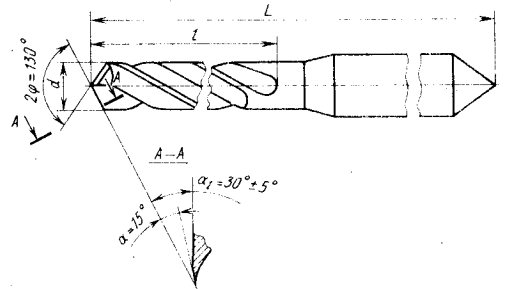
Сверло для обработки отверстий в печатных платах (исполнение 1)
